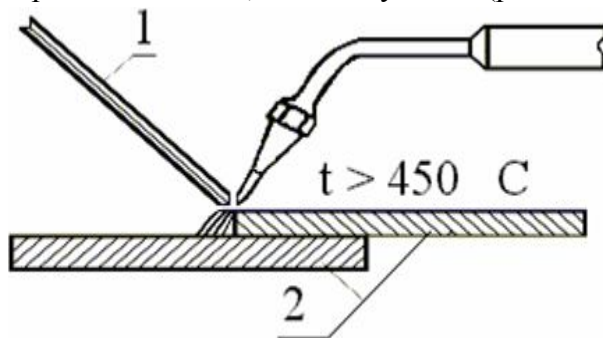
З'єднання деталей пайкою: 1– припой, 2 – деталі
